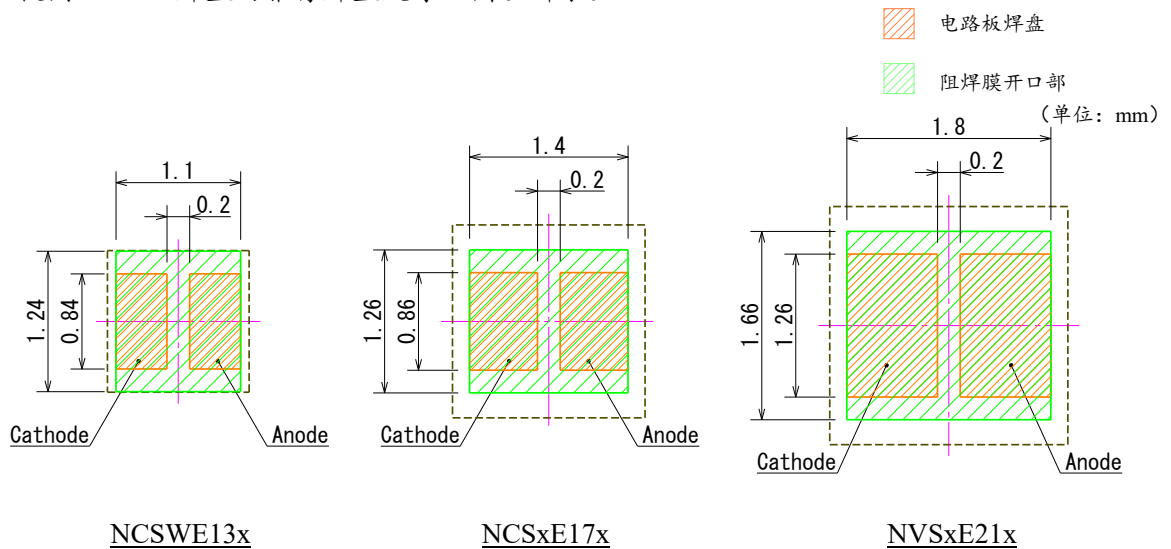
NSMD 焊盘的推荐焊盘尺寸
